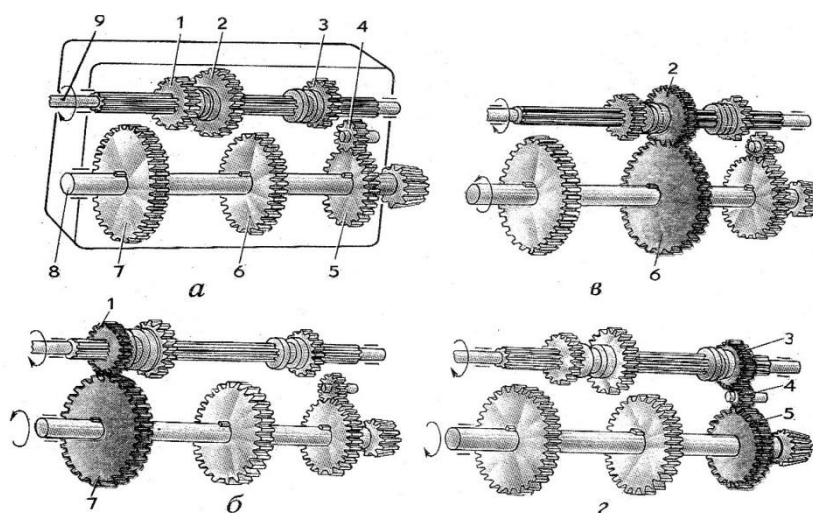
Схема действия коробки передач: а – нейтральное положение; б – включена I передача; в – включена II передача; г – включена задняя передача; 1,2,3 – подвижные шестерни; 4 – шестерня заднего хода; 5,6,7 – неподвижные шестерни; 8 – вторичный вал; 9 – первичный вал
